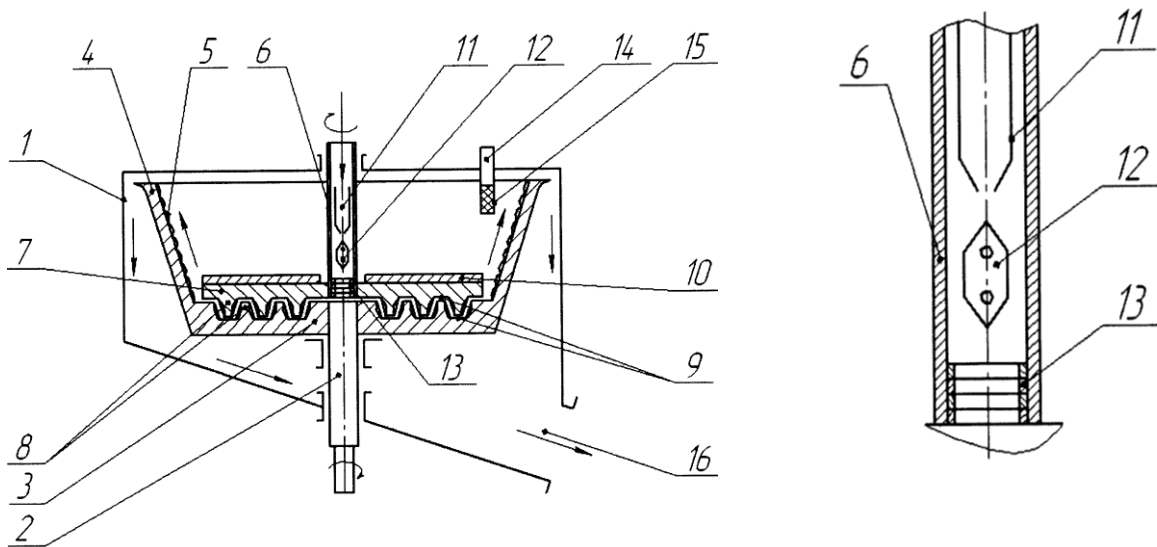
Коллоидная мельница: 1-корпус; 2 и 6- нижняя и верхняя части вала; 3-нижний дисковый ротор; 4-боковое ограждение; 5-магнитная резина; 7- верхний ротор 8- кольцевые выступы 9-кольцевые впадины; 10-лопатки; 11- щелевидное сопло; 12-стальная пластина; 13-кольцевые магниты; 14-сильфон 15- фильтрующий элемент
